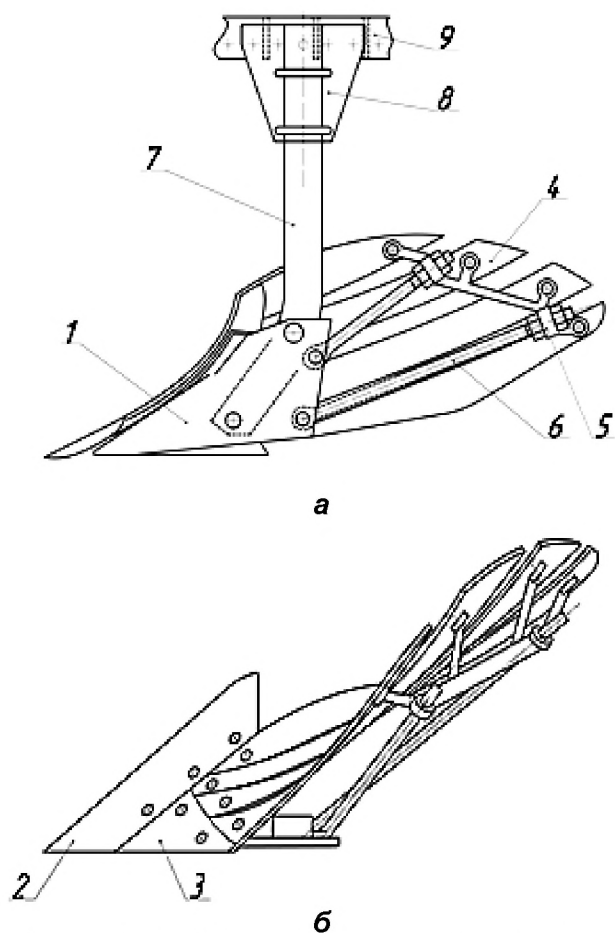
Предплужник лемешный с пластинчатым отвалом: а – вид сбоку; б – вид сверху; 1 – башмак; 2 – лемех; 3 – грудь отвала; 4 – пластина отвала; 5 – кронштейн; 6 – распорка; 7 – стойка; 8 – пластина; 9 – кронштейн
